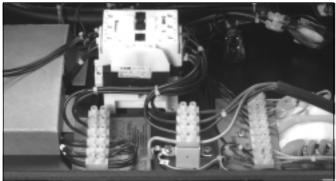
Tablette à bornes des transformateurs de soudage et de commande
